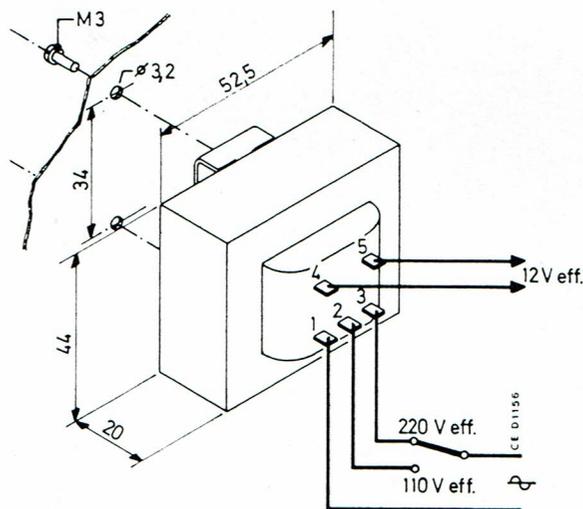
Dimensions du transformateur DY 715 20 (ou 4304 021 24450) à commander séparément
